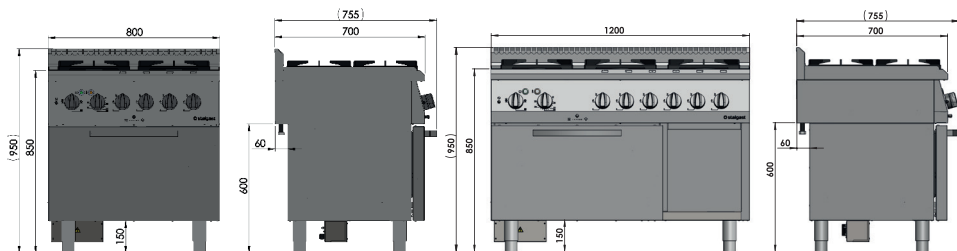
/ Bild. 2 / Fig. 2 / Obr. 2
